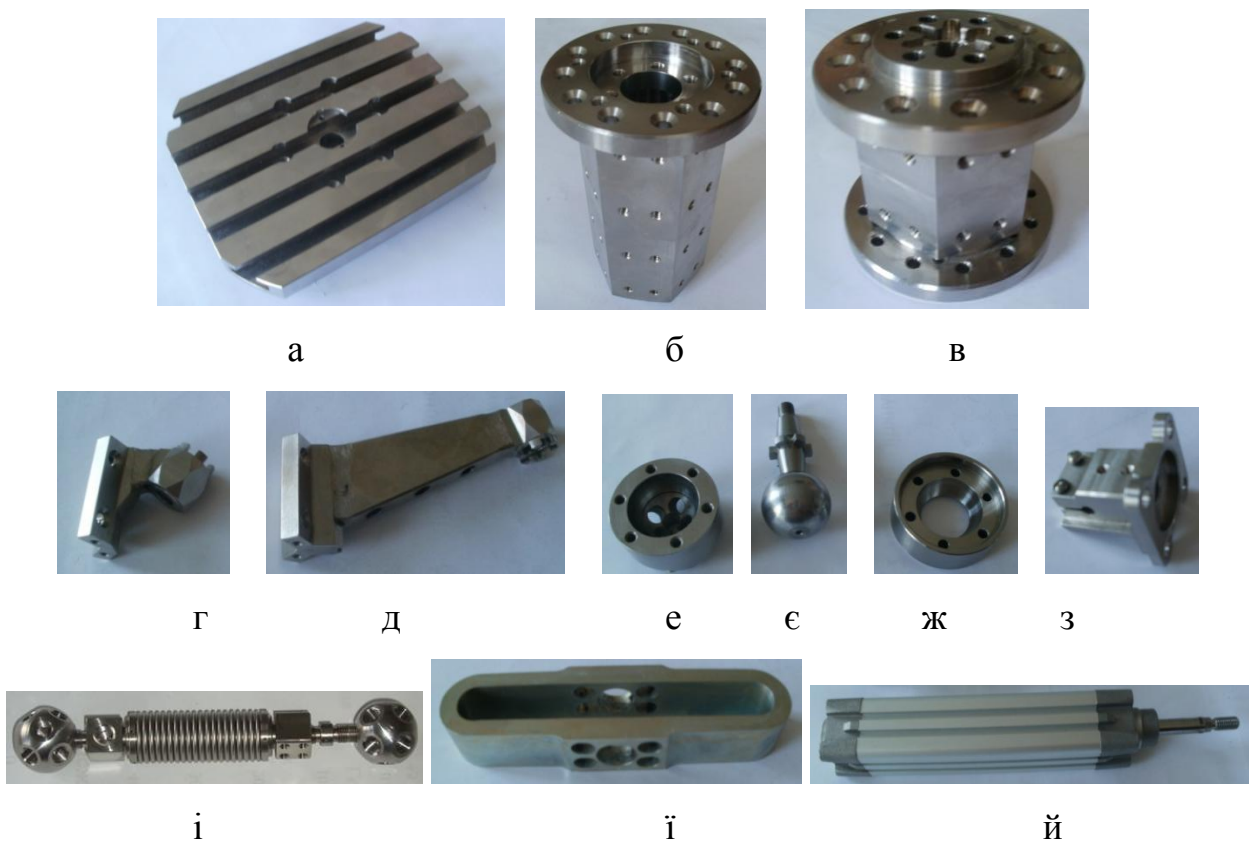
Фото основних деталей, з яких монтуються макетні зразки систем приводів: а – платформа; б – барабан довгий; в – барабан короткий; г – кронштейн короткий; д – кронштейн довгий; е – корпус шарніра; є – хвостовик із сферою; ж – кришка шарніра; з – фланець; і – сифонний привід; ї – пружина; й – пневмоциліндр
